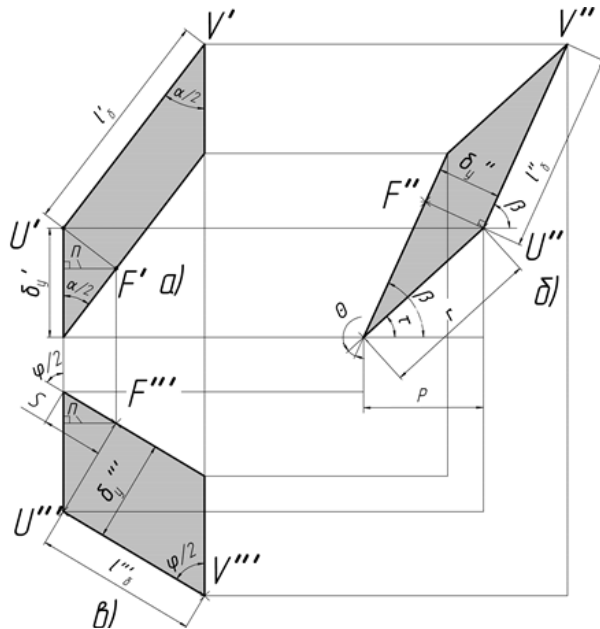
Проекція бокової фаски пера ножа: а) вид спереду; б) вид збоку; в) вид знизу; т. V – вершина пера; U – впадина
